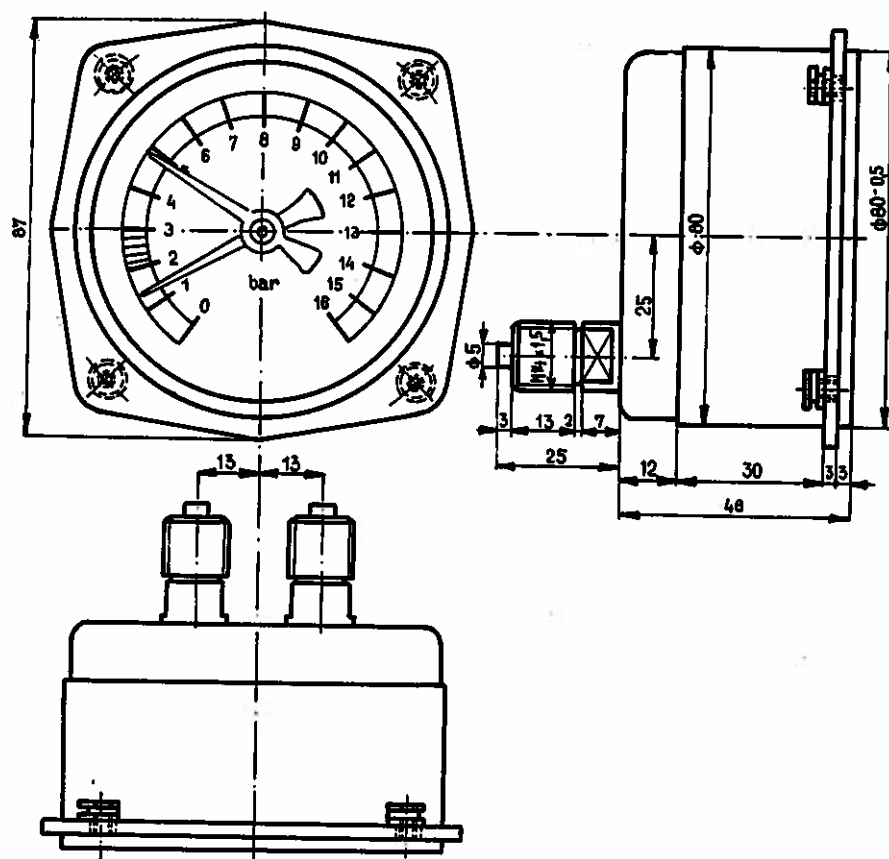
Jednoduchý tlakomer $\varnothing$ 80 mm
